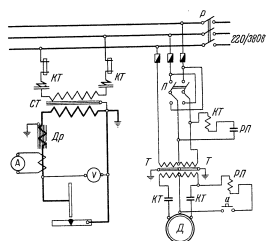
Принципиальная электрическая схема полуавтомата III-5 для сварки на переменном токе
